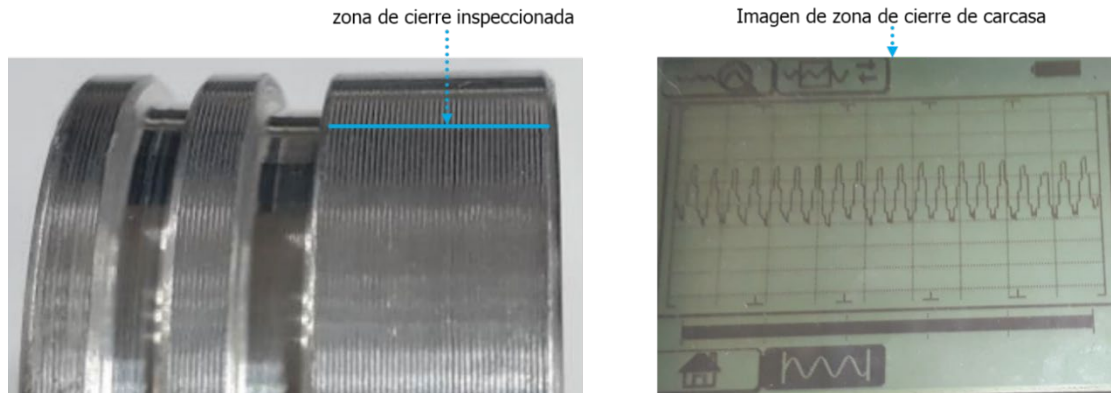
Imagen de zona de cierre detectada por el rugosímetro
